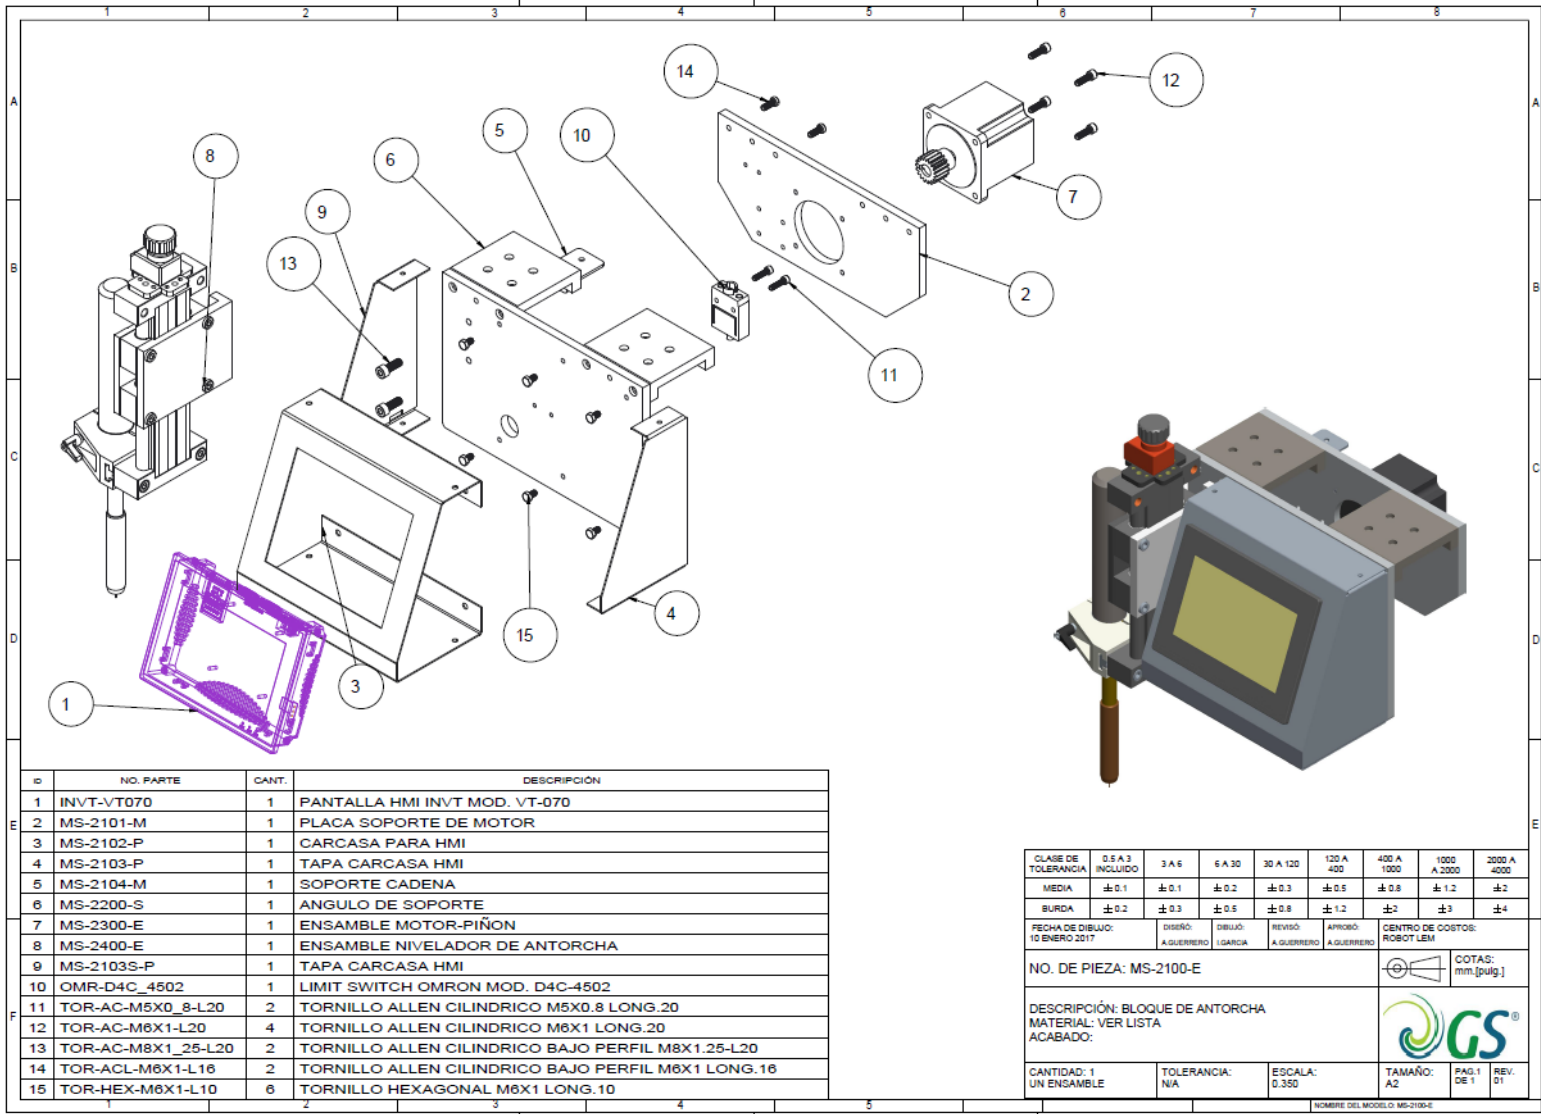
Plano de componentes para soporte de antorcha y pantalla de control de soldadura (cortesía de Green Spare)FR 2 977 469 - B1
